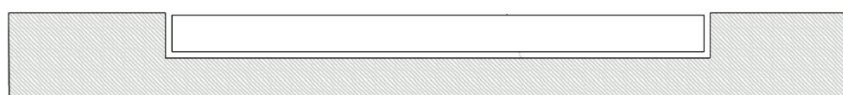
Desenho de corte da madeira da estrutura do contador, parte superior, onde se verifica o rebaixo para a colocação de uma porta batente de um outro objeto. Fonte: el. pr.
